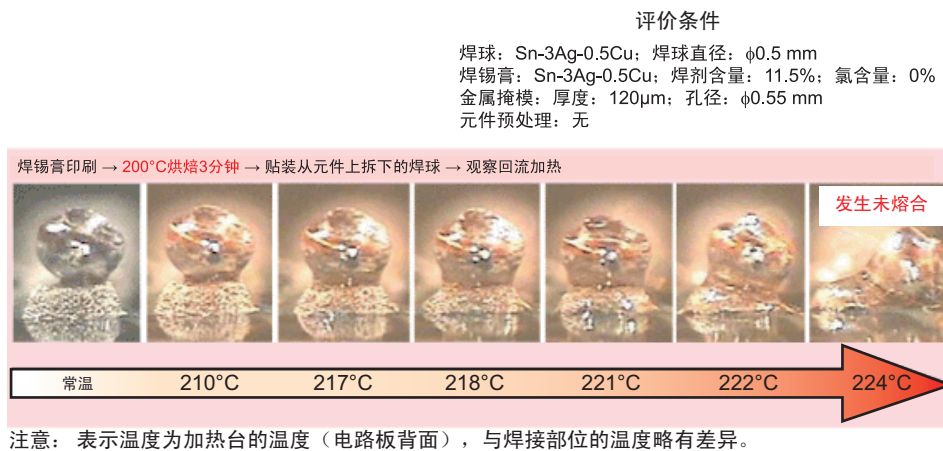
活性降低的焊锡膏形成的焊接
